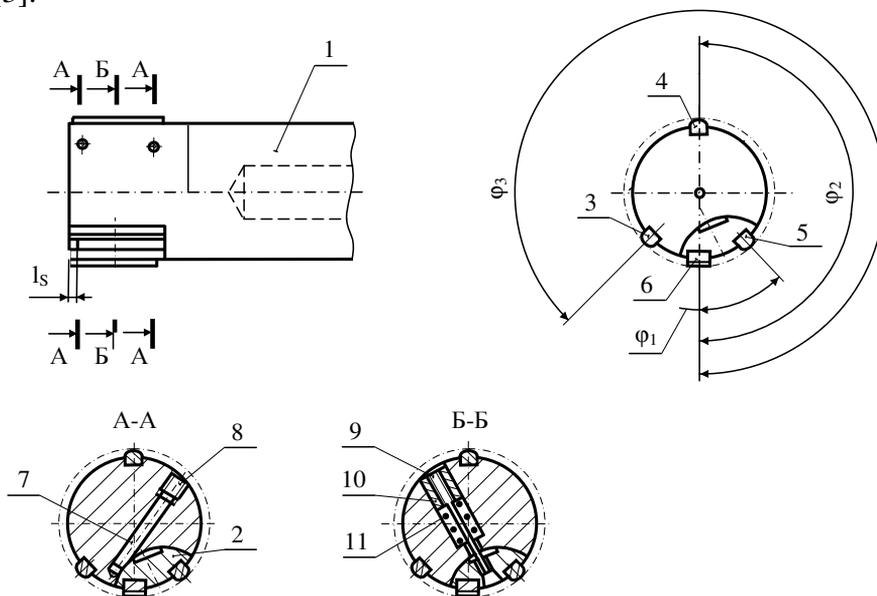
Схема АВР для обработки отверстий: 1 – корпус; 2 – поворотный блок; 3 и 4 – боковой и опорный направляющие элементы; 5 и 6 – направляющий и абразивный элемент, установленные в поворотном блоке; 7 – регулировочные клинья; 8, 9 – винты; 10 – резьбовая втулка; 11 – пружина
